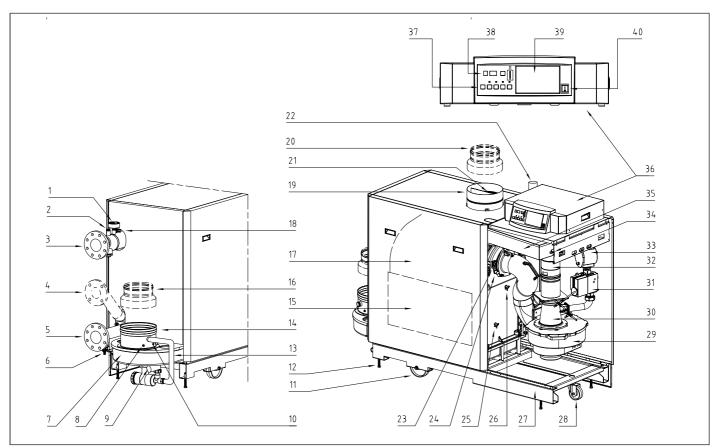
Querschnitt des Remeha Gas 310 ECO 00.31H.79.00002
